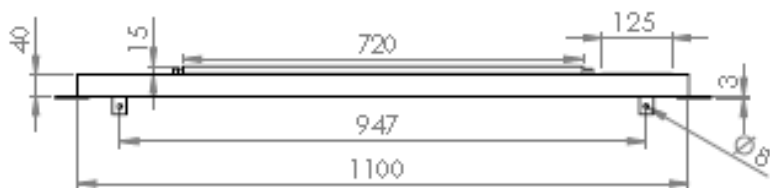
Perfil retangular de 40 x 20 x 1,5 mm
